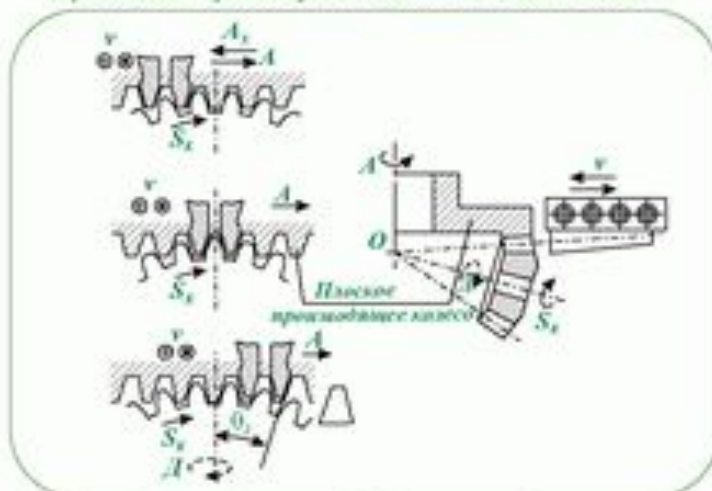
Схемы обработки заготовок на зубофрезерных станках
